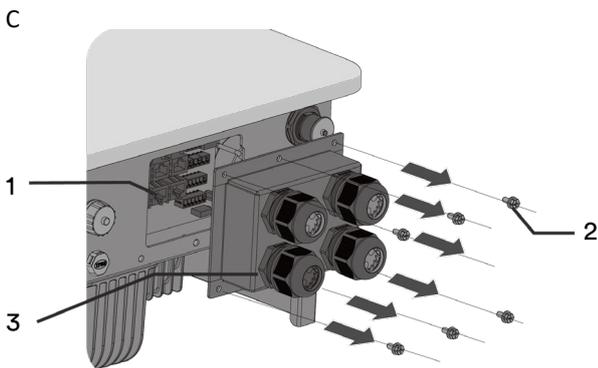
Entfernen der Abdeckung für Schnittstellenanschlüsse.
